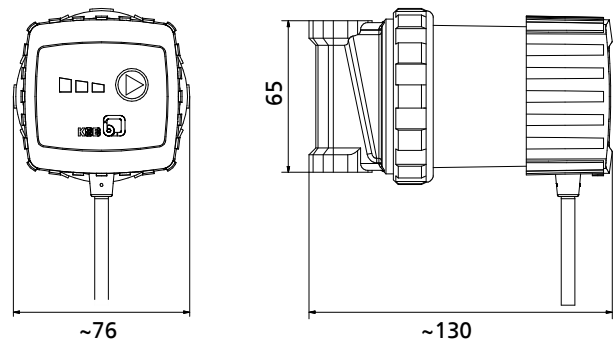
Габаритные размеры Calio-Therm S NC K [мм]
